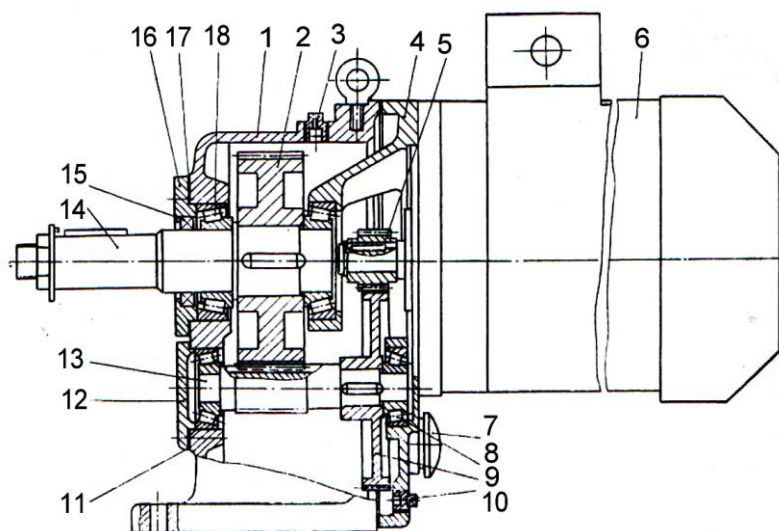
П6 Общий вид мотор-редуктора типа 1МЦ2С
